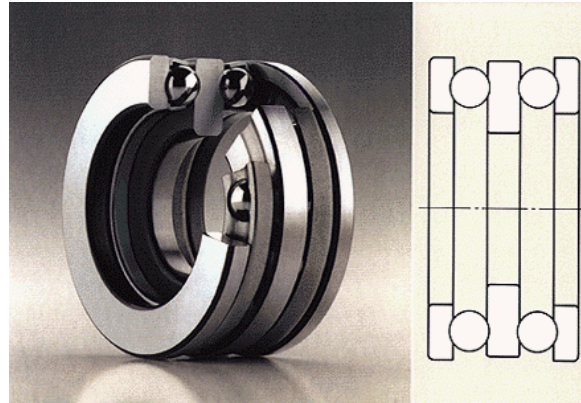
Rodamiento axial de bolas de doble efecto.
